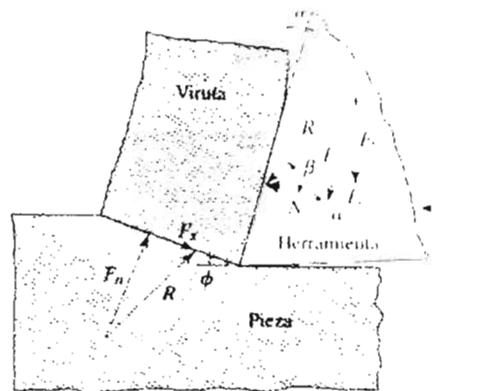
Fuerzas que actúan sobre una herramienta de corte bidimensional.
